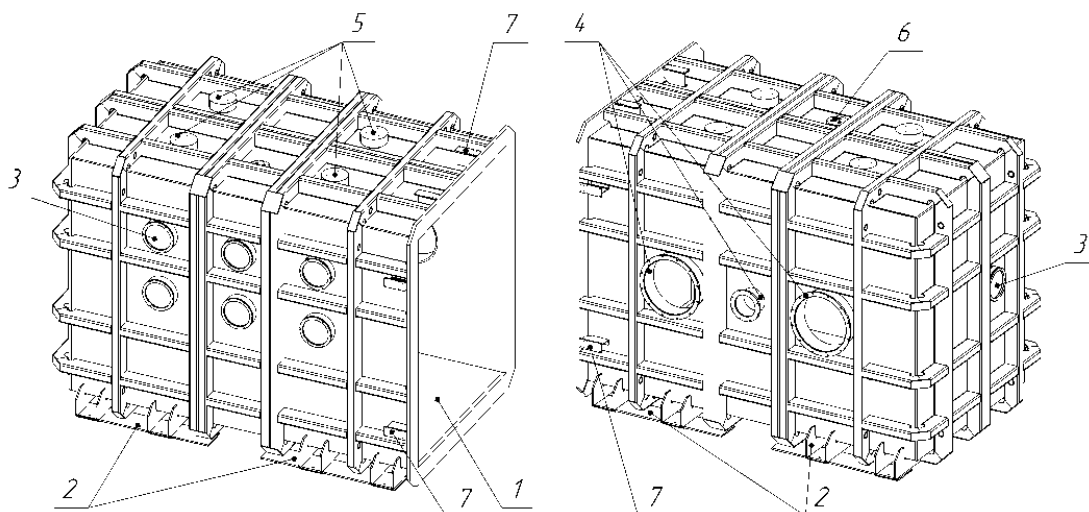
Рабочая камера (1 - корпус, 2 - плита, 3 - иллюминаторы, 4 - патрубок для стыковки вакуумной станции, 5 - фонари, 6 - гермоввод, 7 - пневматический зажим)
